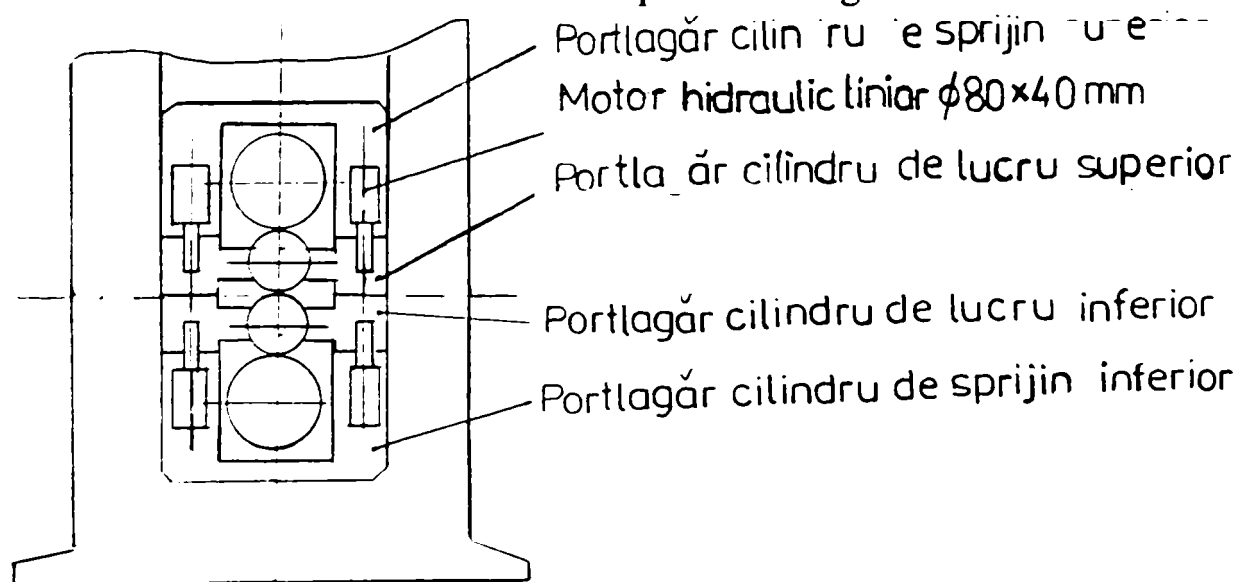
Schema constructivă a sistemului de încărcare negativă a cilindrilor de lucru
